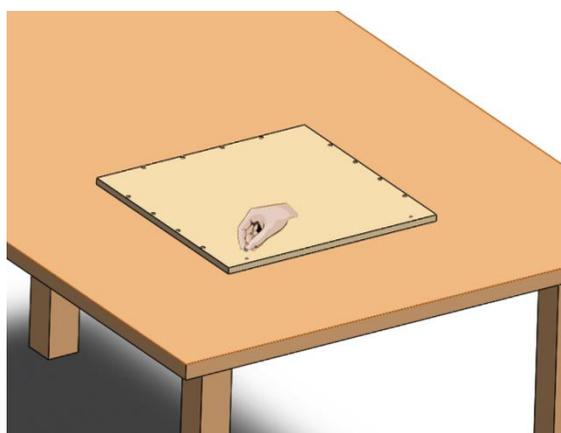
Paso 11 del ensamblaje del cajón (conjunto 2)
